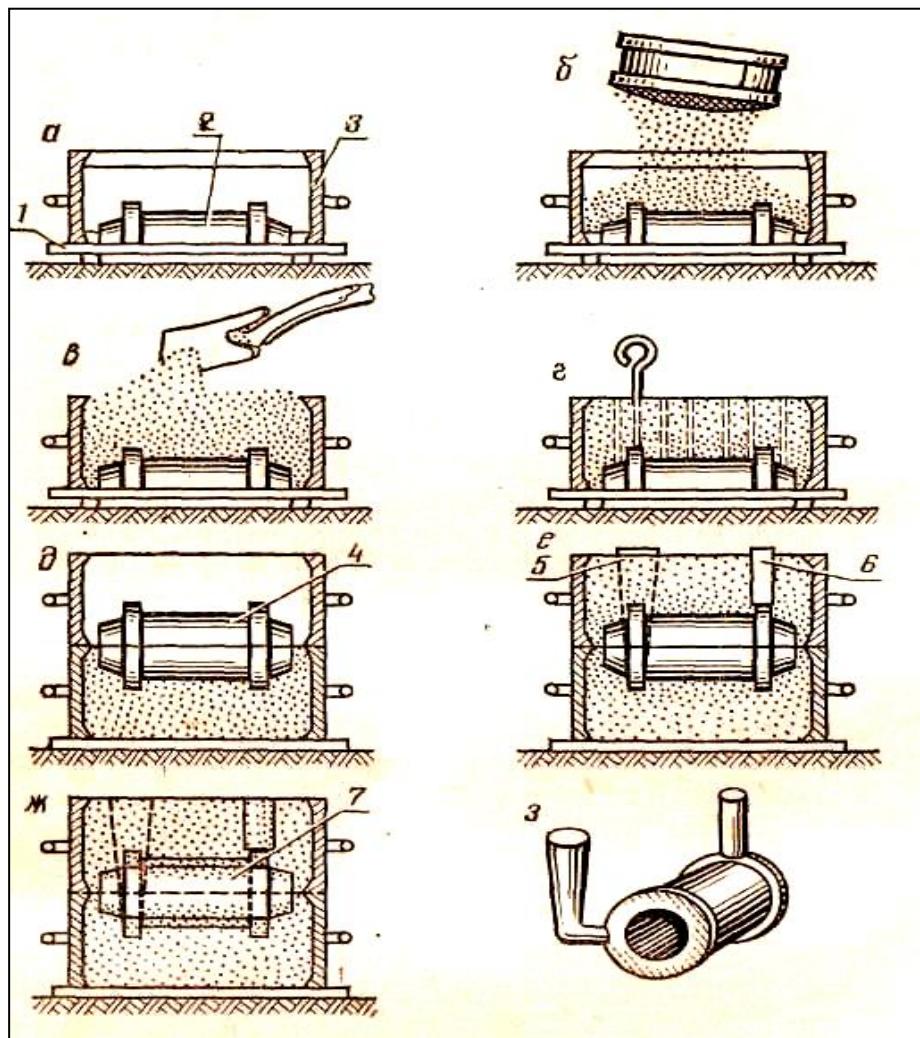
Схема изготовления отливки: 1- ; 2- ; 3- ; 4- ; 5- ; 6- ; 7- ; 8- ; а-3 -
